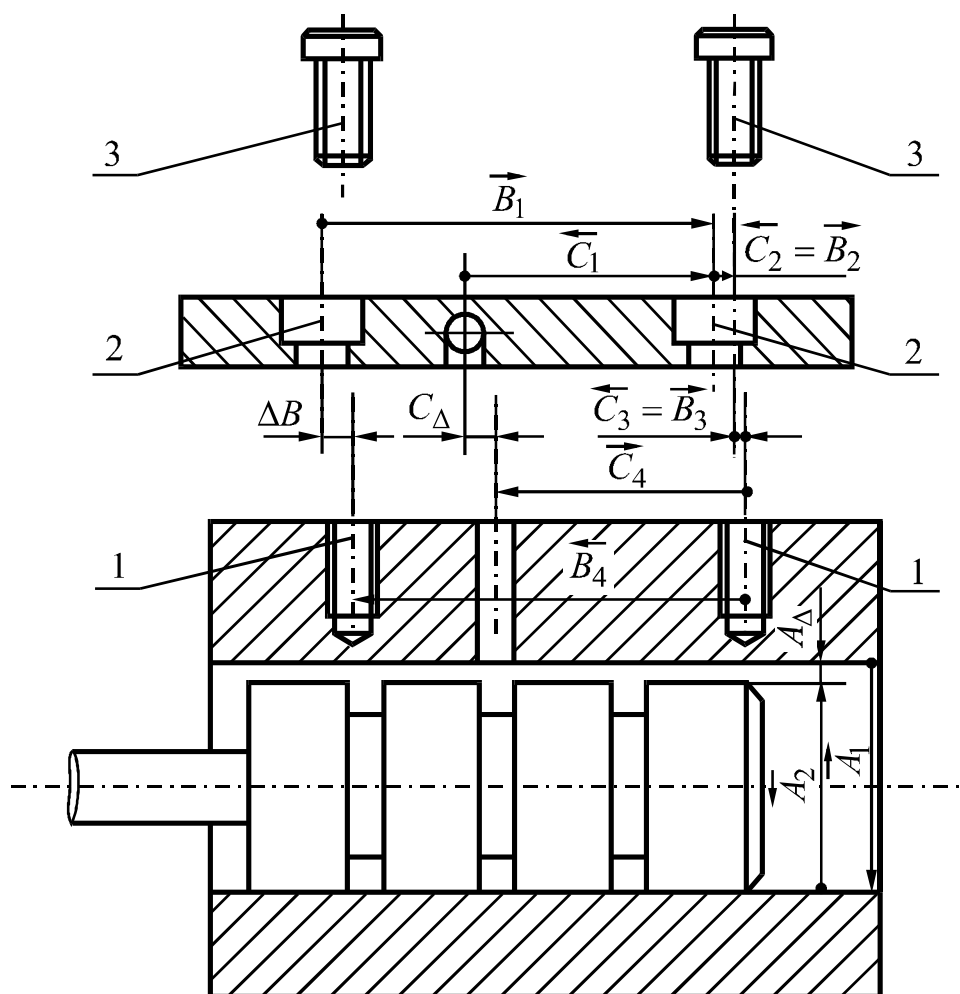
Сборочные размерные цепи золотникового устройства: 1 – ось резьбового отверстия в конусе золотника; 2 – ось отверстия в крышке; 3 – ось винта (A – размерная цепь обеспечения плавного, с заданной посадкой, перемещения золотника; C – размерная цепь обеспечения совмещения с заданной точностью осей каналов в крышке и корпусе золотникового устройства; B – размерная цепь обеспечения собираемости крышки золотника и корпуса с помощью крепежных винтов)
